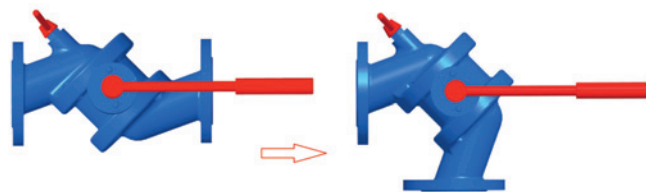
Запорно-регулирующий шаровой кран с регулируемым поджатием и изменяемой геометрией корпуса
